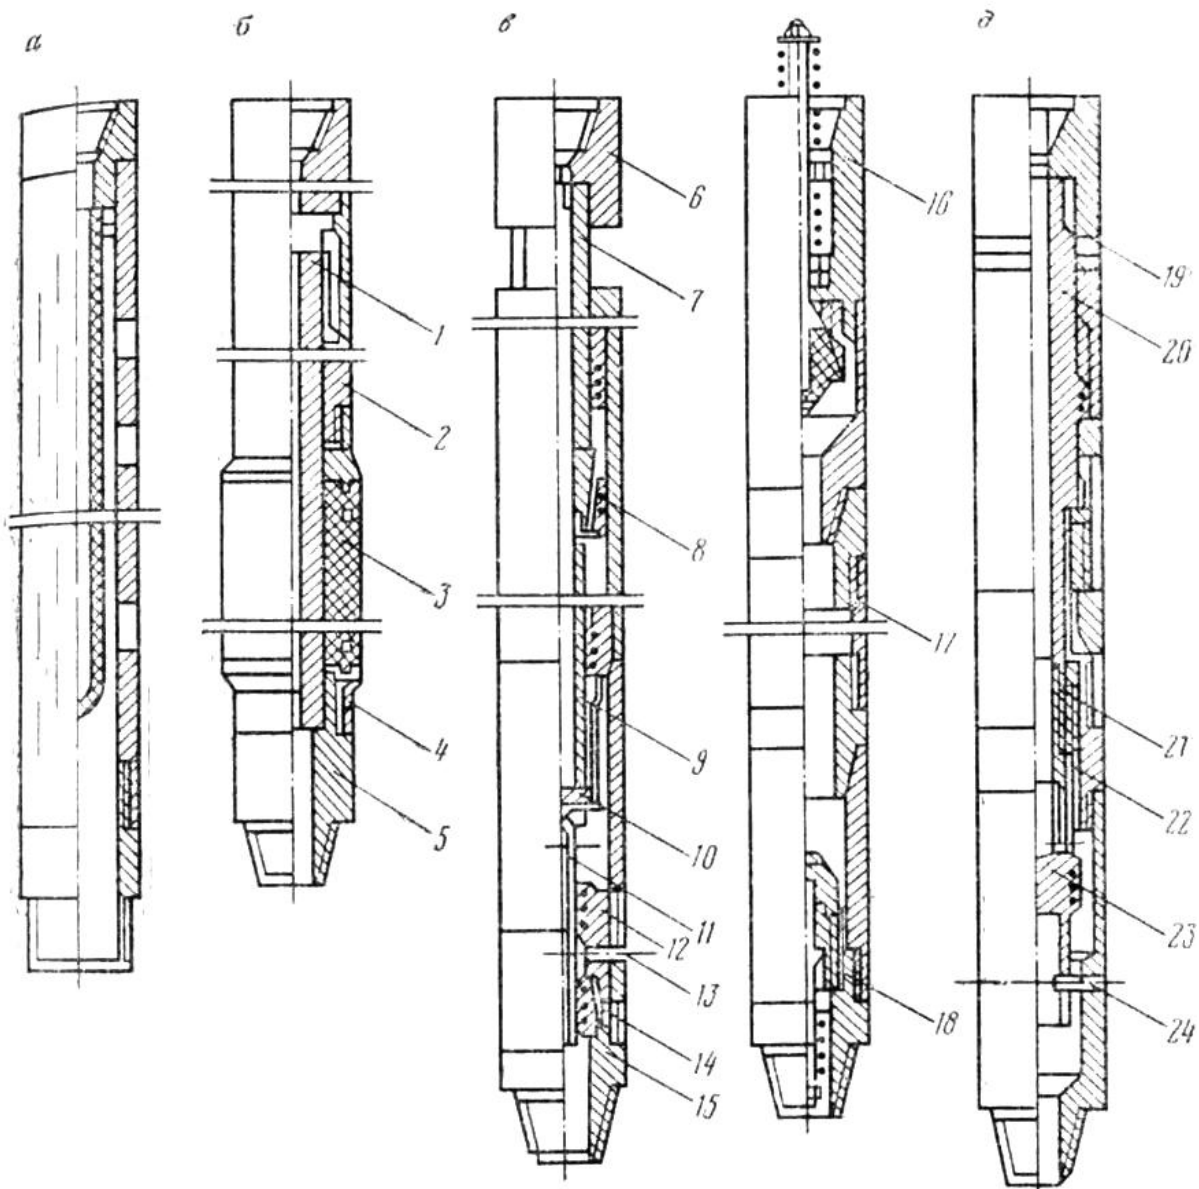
Схема приладів комплексу випробувальних інструментів КВІ-65: а – подвійний фільтр Ф-65; б – пакер циліндричний ПЦ-65; в – випробувач пластів гідравлічний ВПГ-65; г – пробовідбірна камера конструкції УкрНДГаза; д – клапан запірний поворотний ЗП-95
